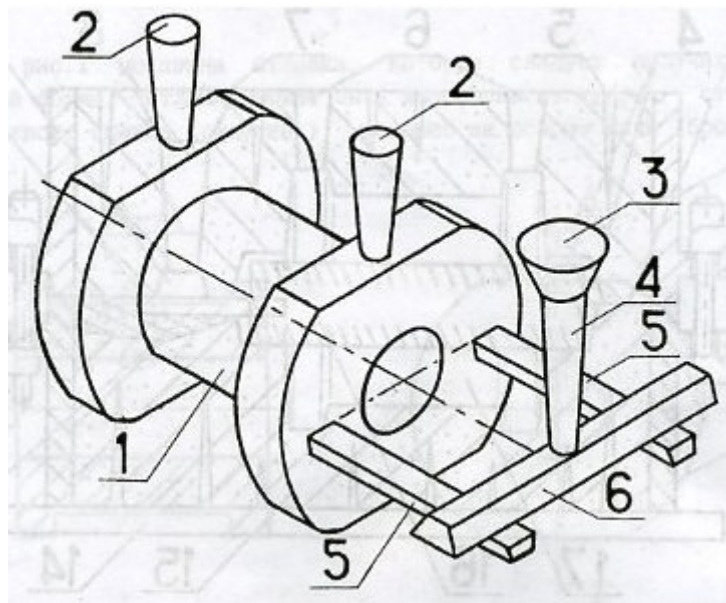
Эскиз отливки с элементами литниковой системы
